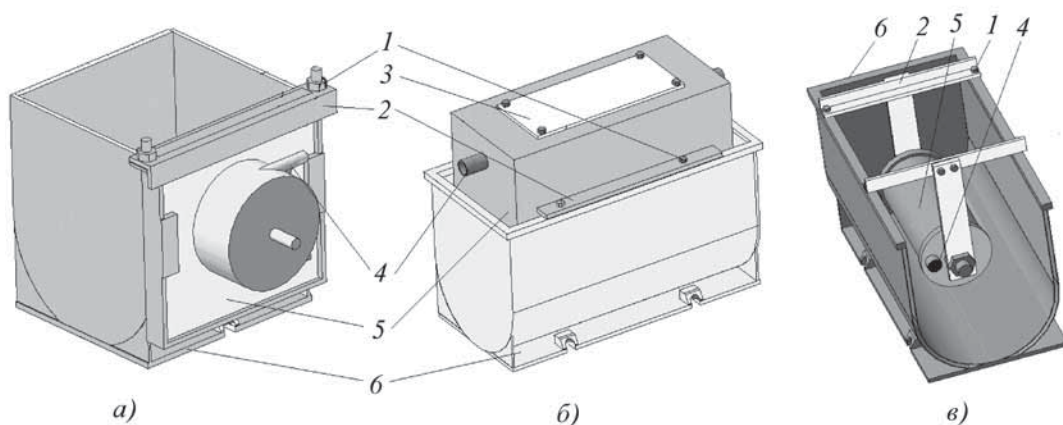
Конструкция рабочей камеры для виброультразвуковой обработки деталей в свободном состоянии с расположением ультразвукового преобразователя:
